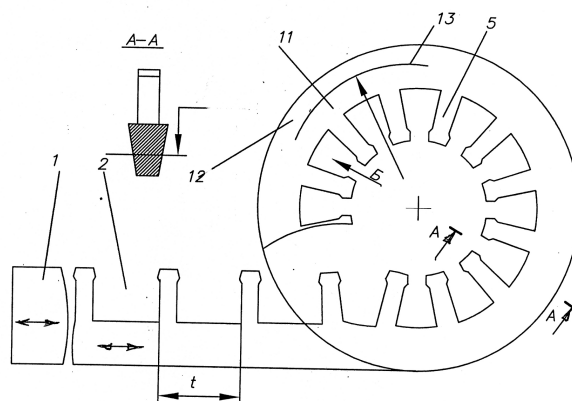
Схема изготовления витых магнитопроводов статоров, предложенная фирмой General Electric Co., США
